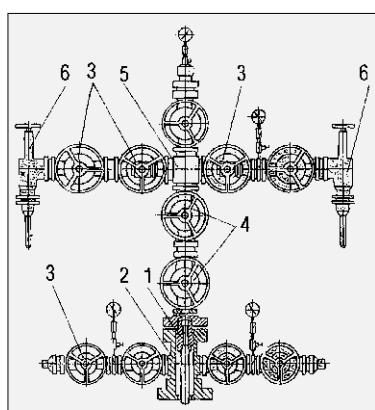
Схема фонтанной арматуры на давление 70 МПа в сборе:
